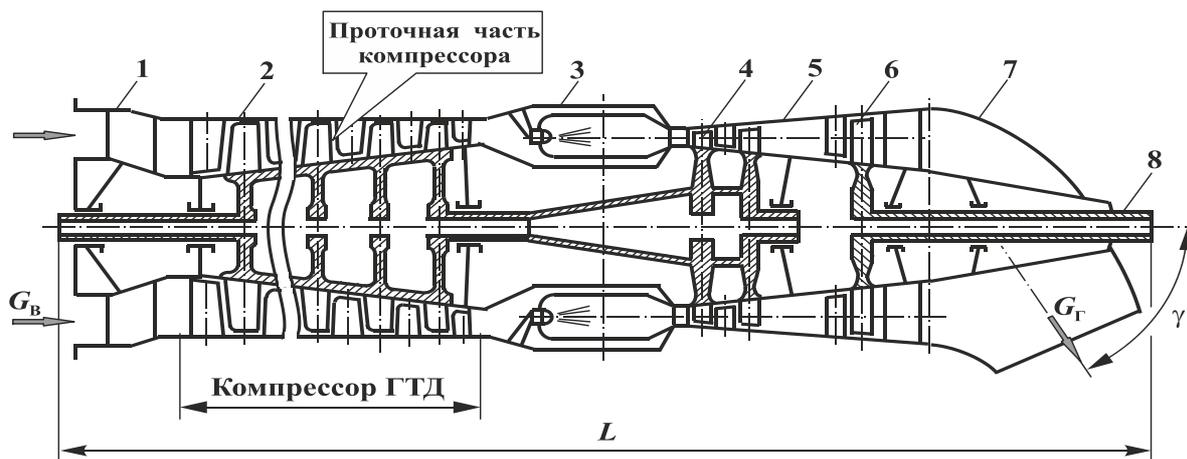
Схема вертолетного ГТД со свободной турбиной и одновальным газогенератором: 1 – входное устройство, 2 – осевой компрессор, 3 – камера сгорания, 4 – турбина компрессора, 5 – переходник, 6 – свободная турбина, 7 – выпускной канал, 8 – вал отбора мощности
